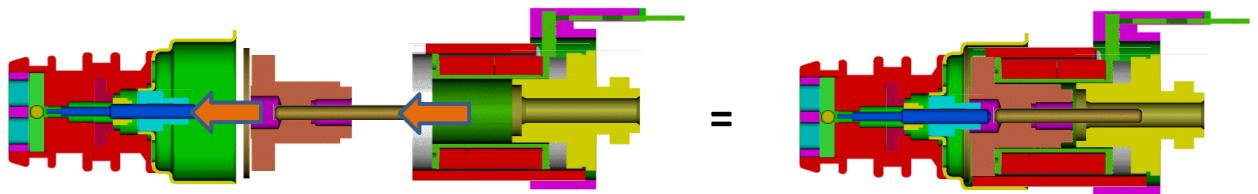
Ensamble de Flange y Grupo magnético 326.
